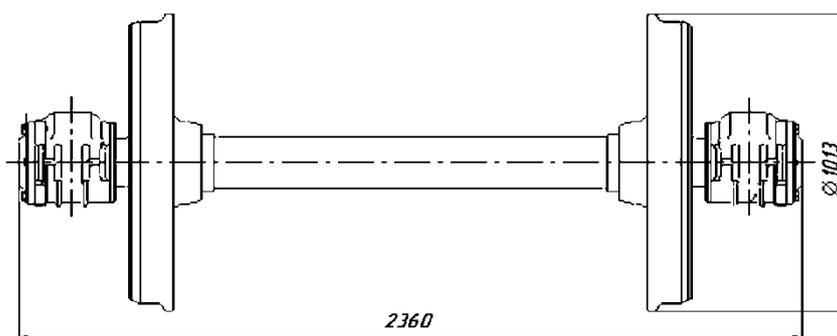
Колесная пара типа РУ1Ш-957-Г с подшипниками в корпусе буксы
